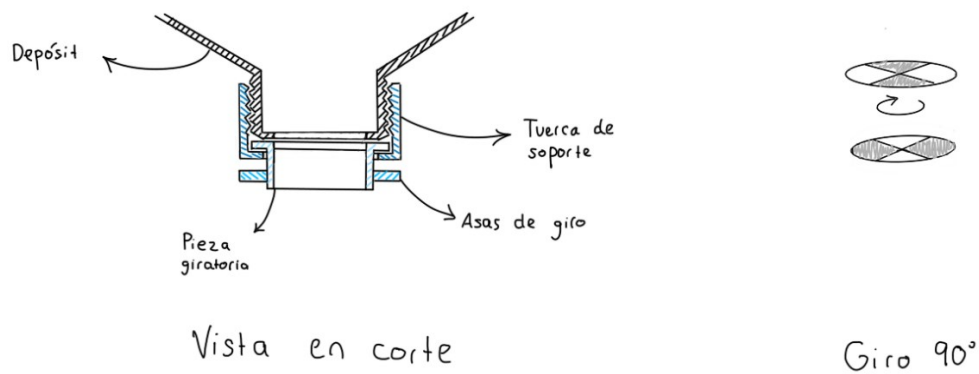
Sistema de alimentación de compuerta giratoria - Vistas de detalle
